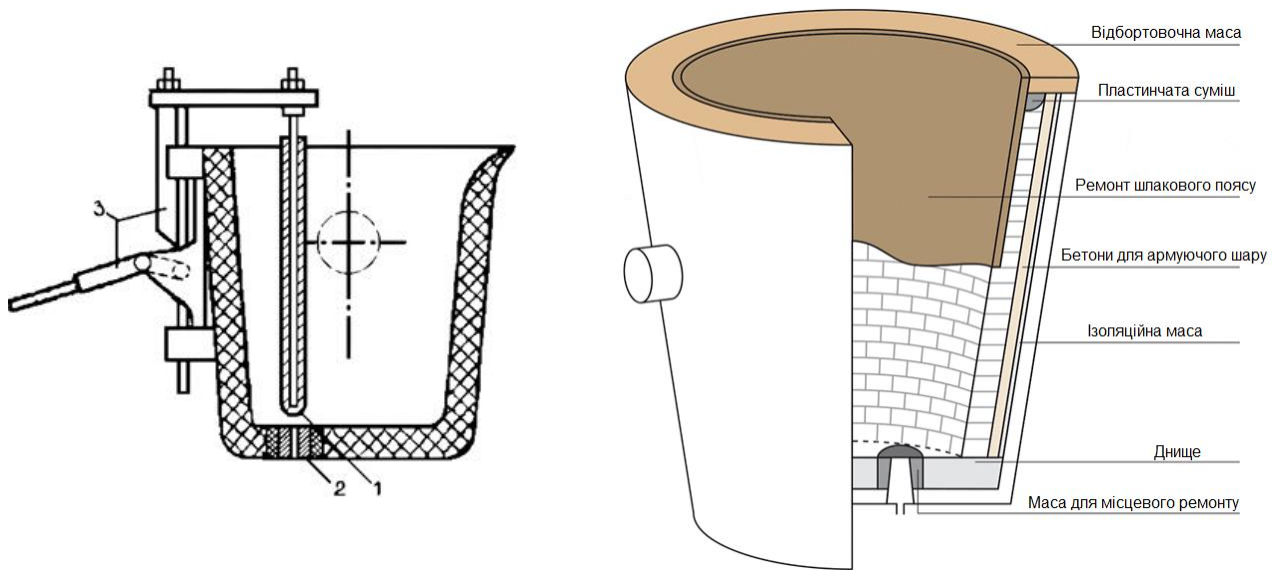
Сталерозливальний ківш зі стопорним затвором: 1 - стопор; 2 - стакан з отвором для випуску сталі; 3 - важільна система керування стопором
